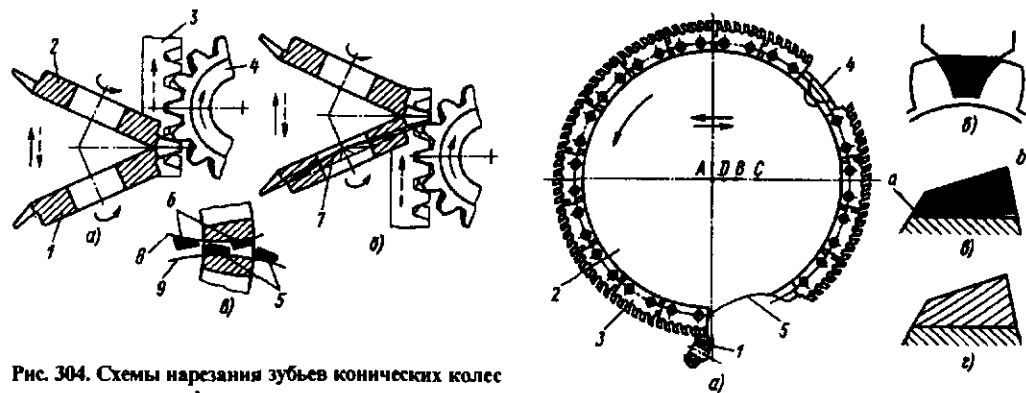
Схемы нарезания зубьев конических колес двумя дисковыми фрезами
